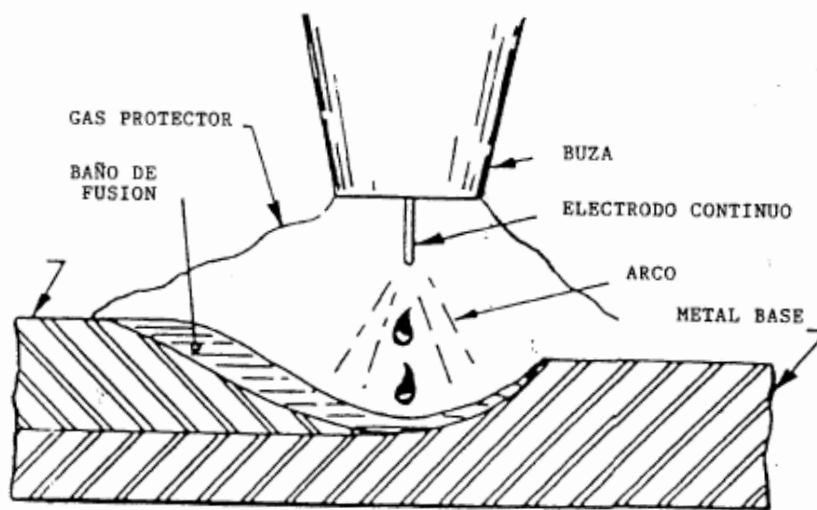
Elementos que intervienen en la soldadura G.M.A.W.
